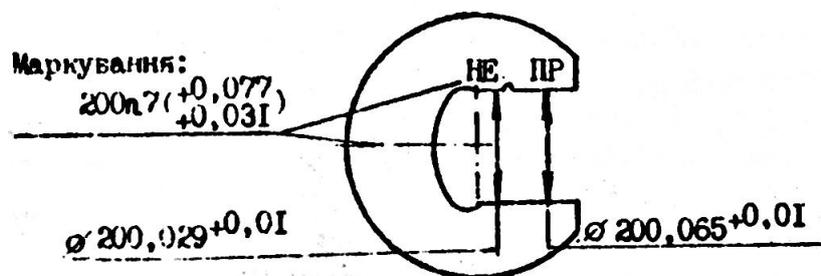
Калібр-скоба для контролю вала Ø200 h7
